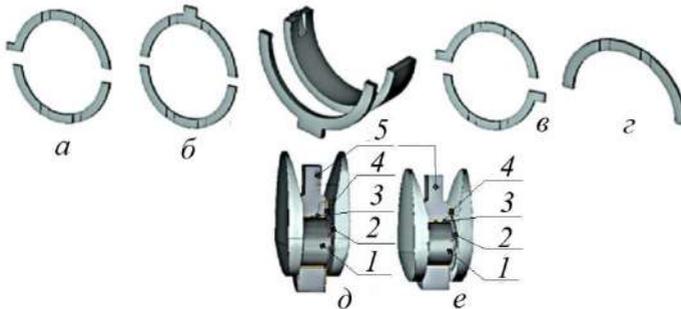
Схема упорного підшипника з півкільцями:
